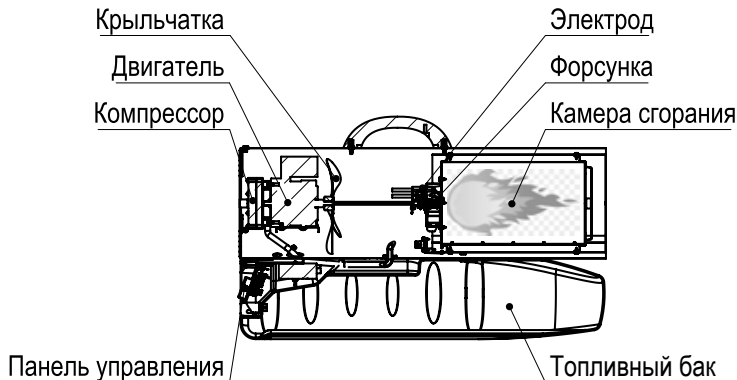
Устройство тепловентилятора компрессорного типа
